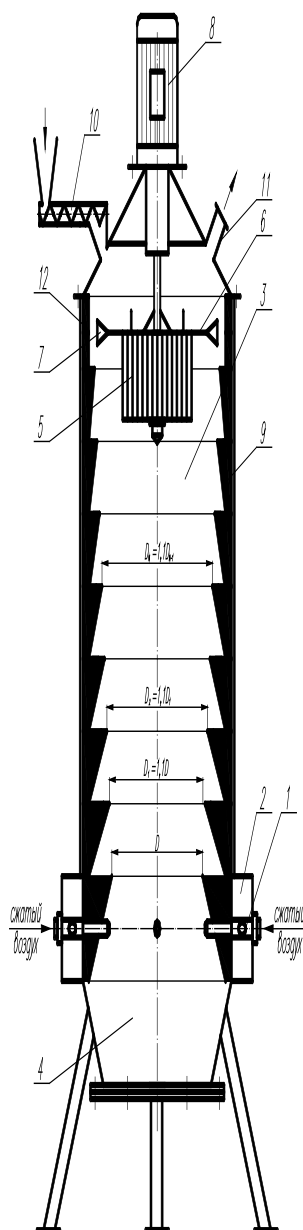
Схема струйной мельницы с цилиндрической камерой помола
